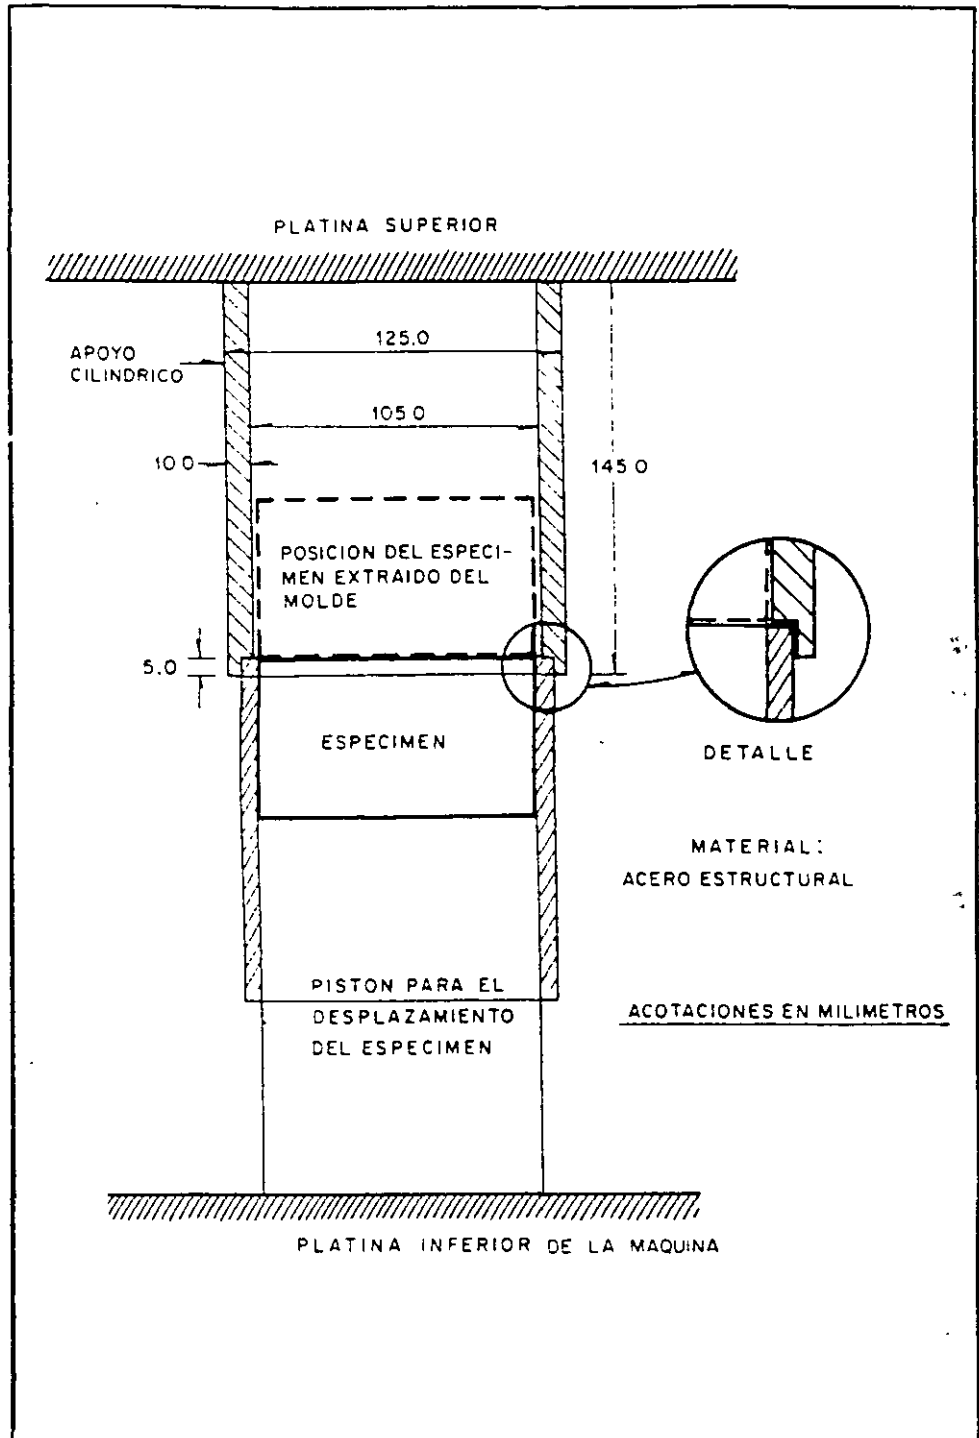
APOYO CILINDRICO MONTADO, PARA SACAR ESPECIMENES DEL MOLDE.
